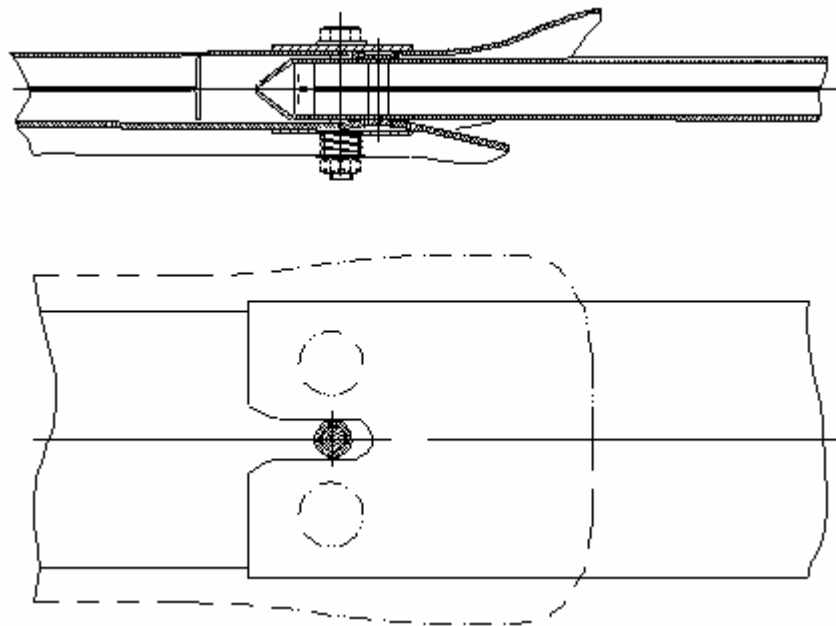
Внутренний фиксирующий ловитель включенного положения полуножей разъединителя
